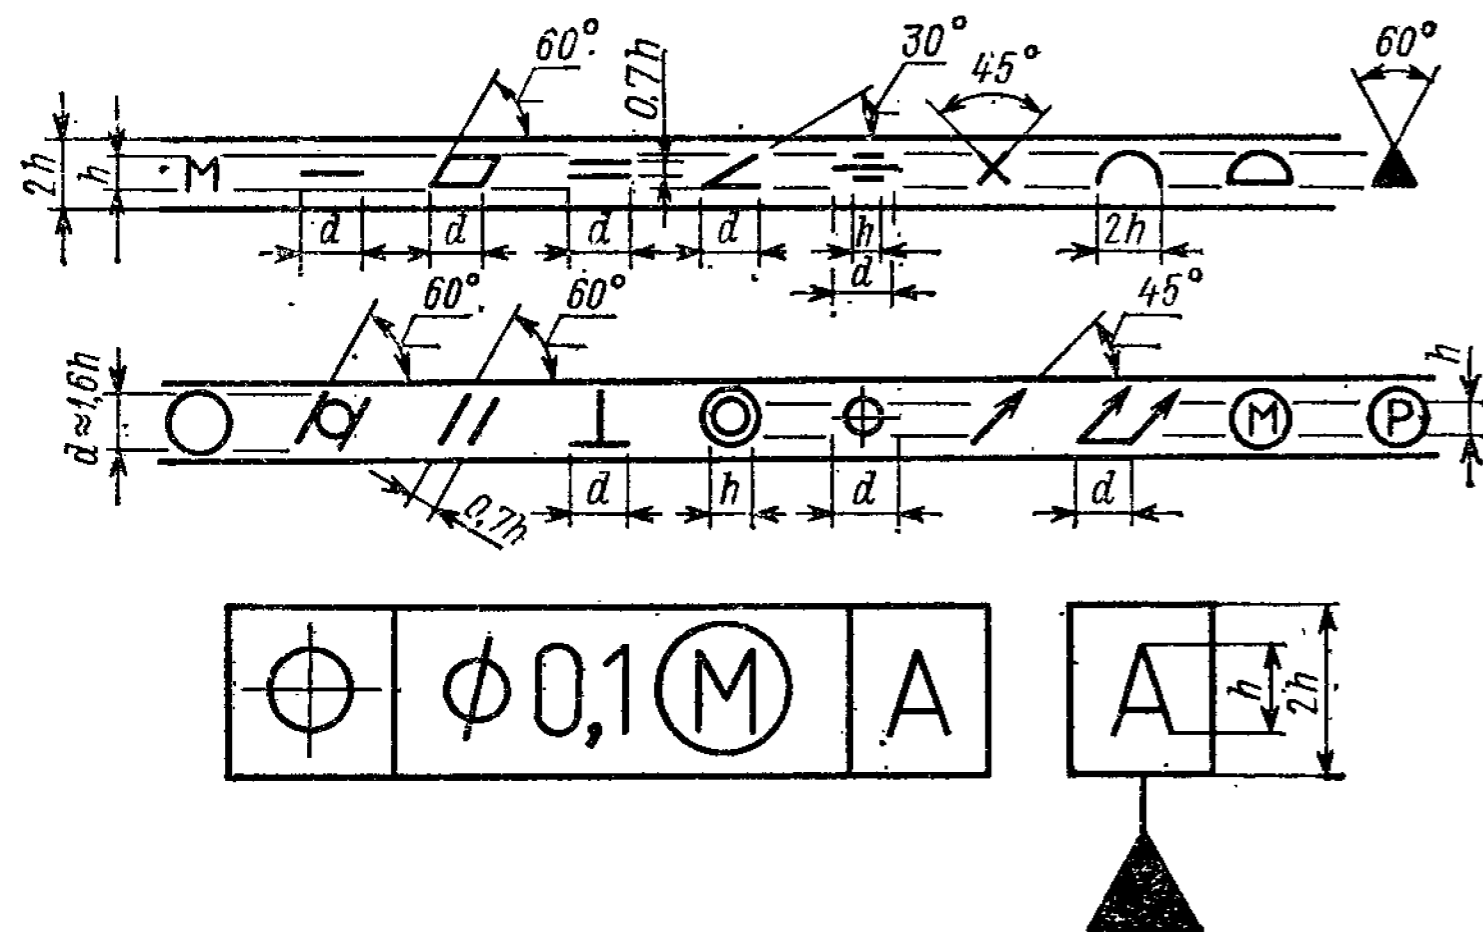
Форма и размеры знаков для обозначения допуска формы и расположения ( $h$  и  $d$  — высота и ширина шрифта размерных чисел)
